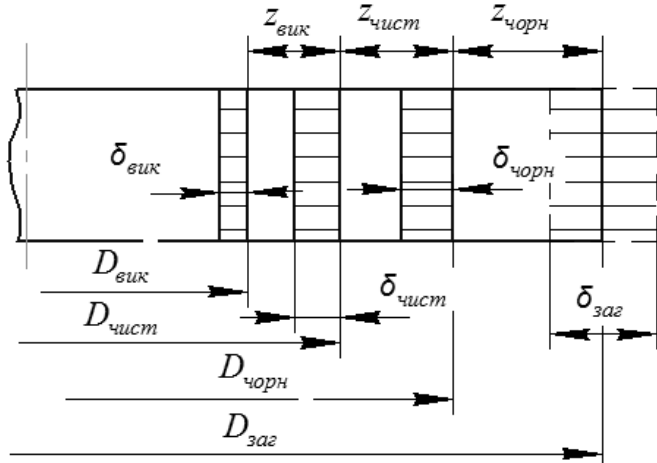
Схема розміщення припусків і допусків при багаторазовій обробці зовнішньої поверхні обертання
